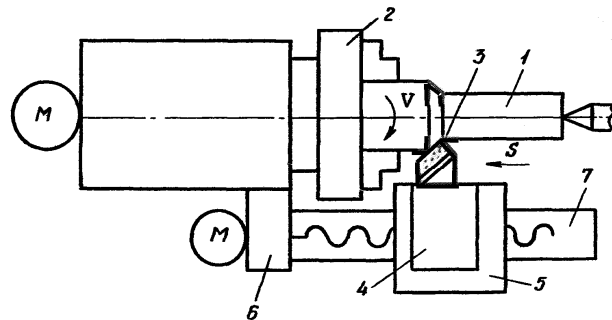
Схема привода подачі токарного верстата з дискретним переміщенням супорта по напрямних
